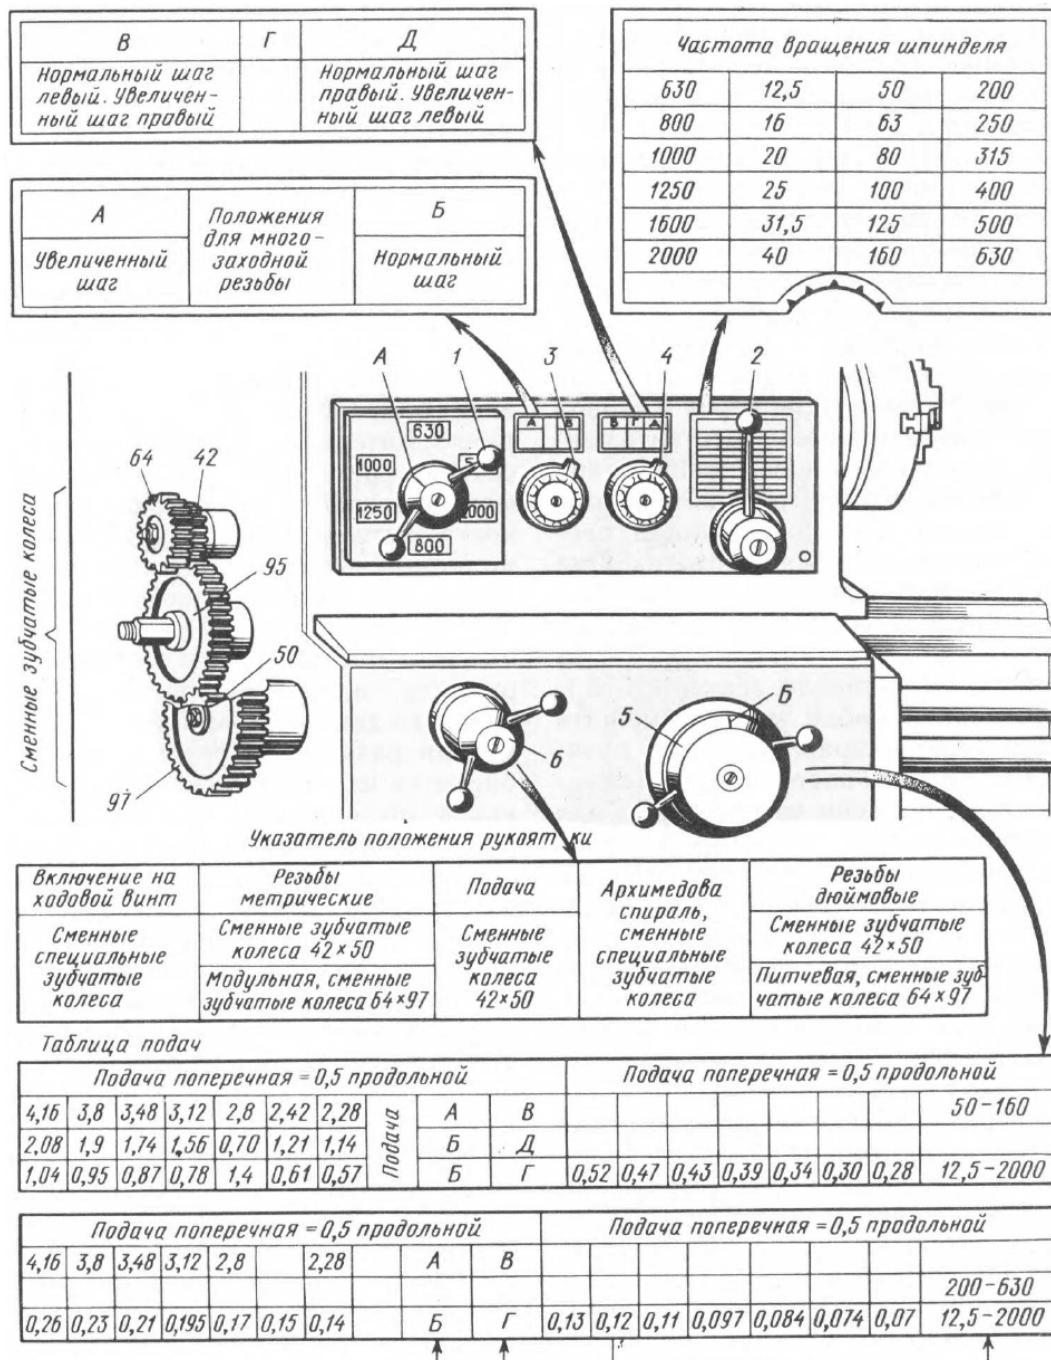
Показчики положения і настройки на передній бабці токарного верстата 1К62
